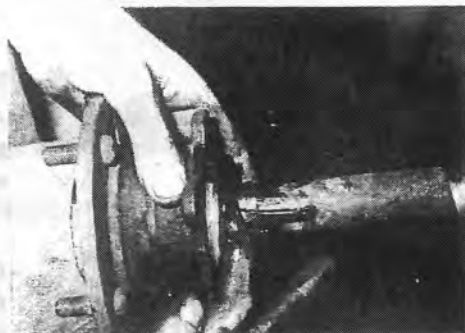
; Nu kan met een haakje de binnenste lagerschaal verwijderd worden. Dit kan enige kracht vergen. Ben voorzichtig het oppervlak niet te beschadigen.
